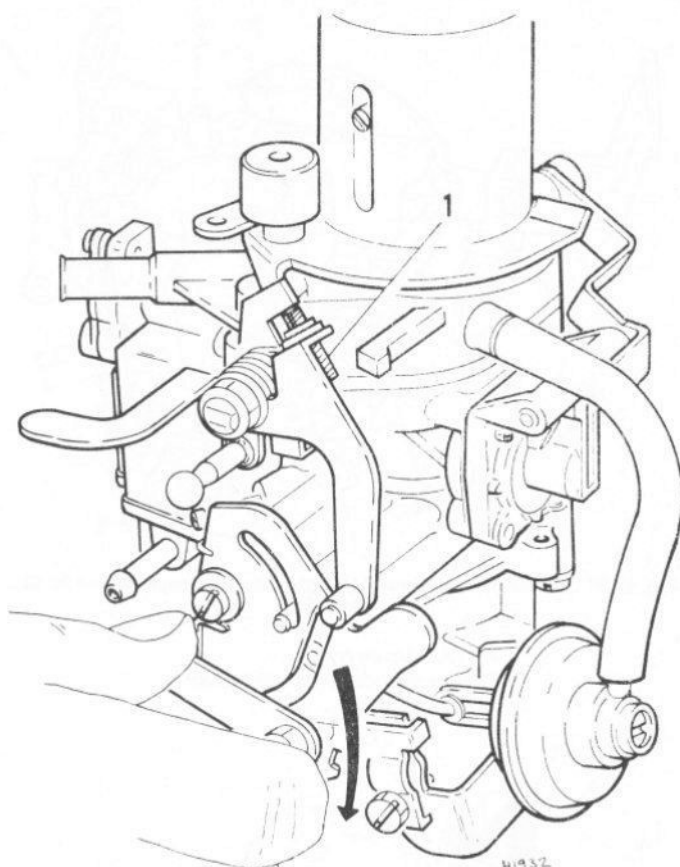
Régler le ralenti accéléré à l'aide d'un calibre coudé - carburateur Weber 35 IBSH (Sec 8)
